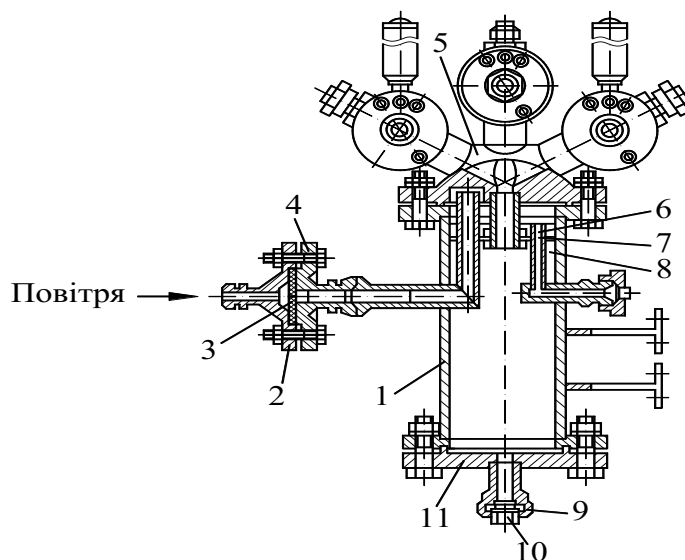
Установка: 1 – корпус фільтра; 2 – кришка клапана; 3 – мембрана; 4 – корпус клапана; 5 – блок камер згорання; 6 – зливний патрубок; 7 – механічний дисковий фільтр; 8 – вода; 9 – гайка; 10 – заглушка; 11 – кришка фільтра.
